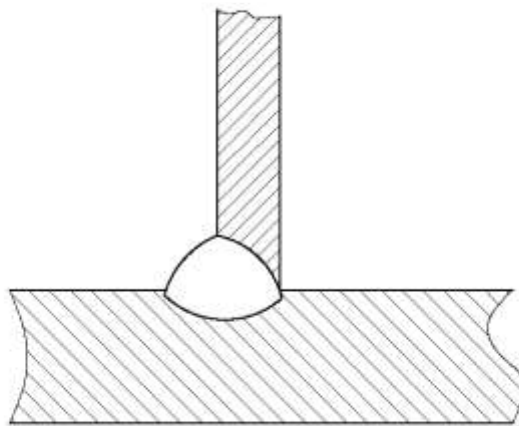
Загальний вигляд таврового зварного шва
